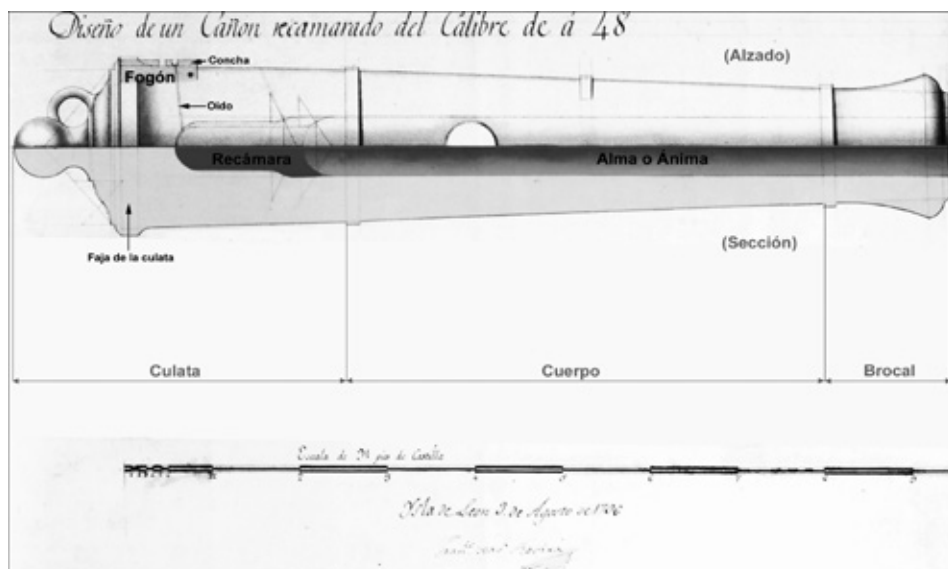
Alzado / sección de un cañón de 48 libras, recamarado. M.N.M., Mss. 608.
